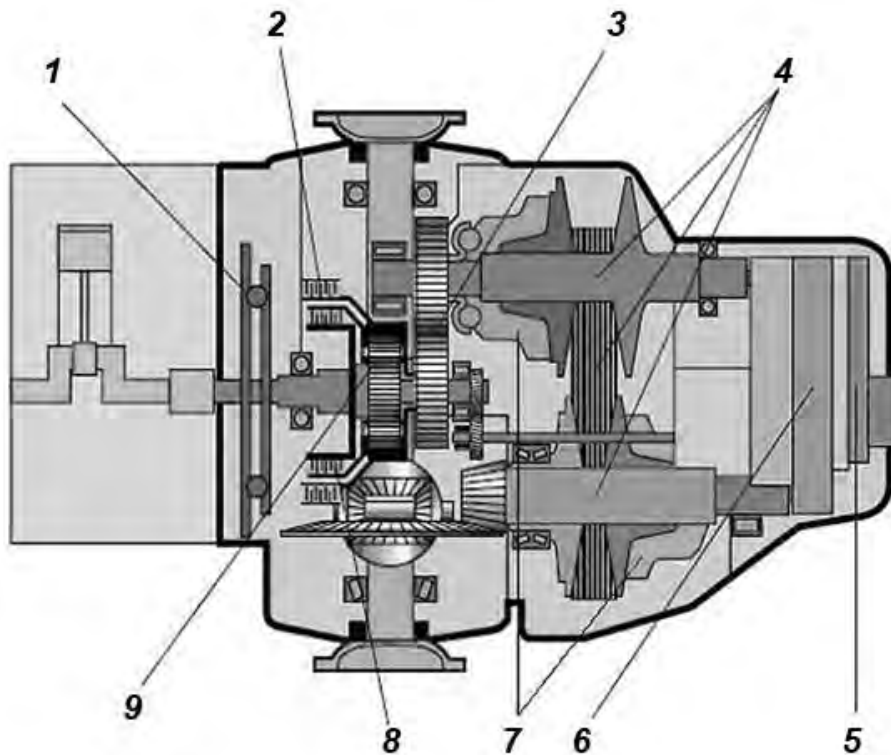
Принципова схема сучасної варіаторної коробки передач
